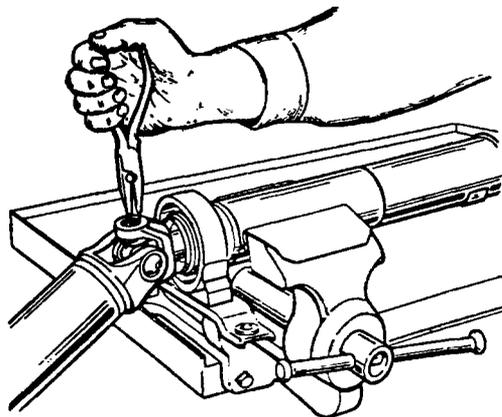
Извлечение стопорных колец подшипников крестовины
